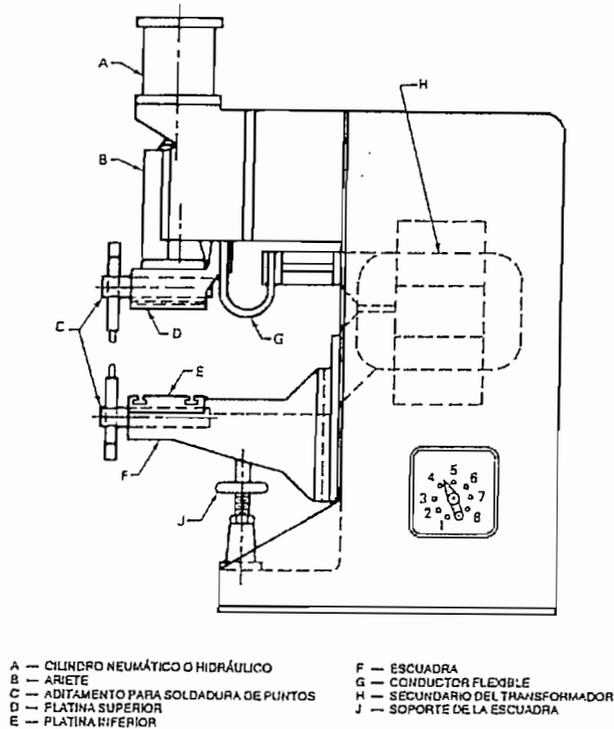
SOLDADORA TIPO PRENSA
